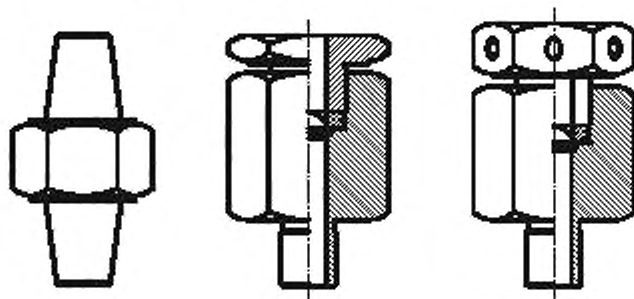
Типовые держатели разрывных мембран в виде резьбовой пробки
